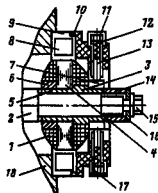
Конструкция и способ соединения тахогенератора ТП80-20-0,2 с двигателем. 1 — обмотка якоря, 2 — вал двигателя, 3 — втулка, 4 — сердечник якоря, 5 — шайба, 6 — кольцо, 7 — коллектор, 8 — магнит, 9 — сегмент кольца, 10 — щеткодержатель, 11 — обойма щеткодержателя, 12 — пружина, 13 — щетка, 14 — втулка, 15 — гайка, 16 — шайба, 17 — винт, 18 — подшипниковый щит двигателя
